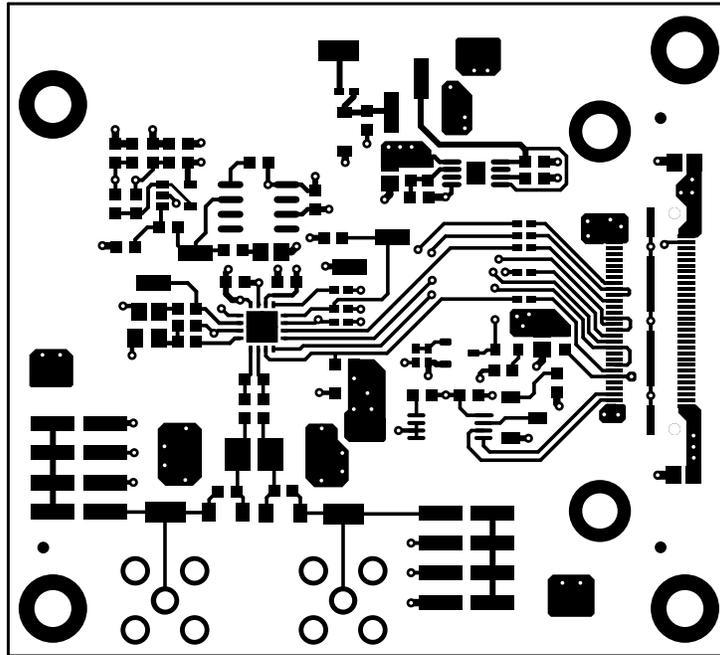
ADS8681WEVM PCB 第 1 层 - 顶层
